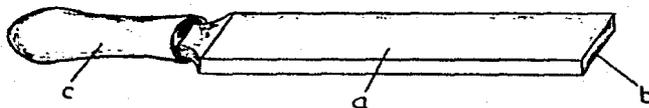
Partes de la rasqueta. a) Cuerpo;
